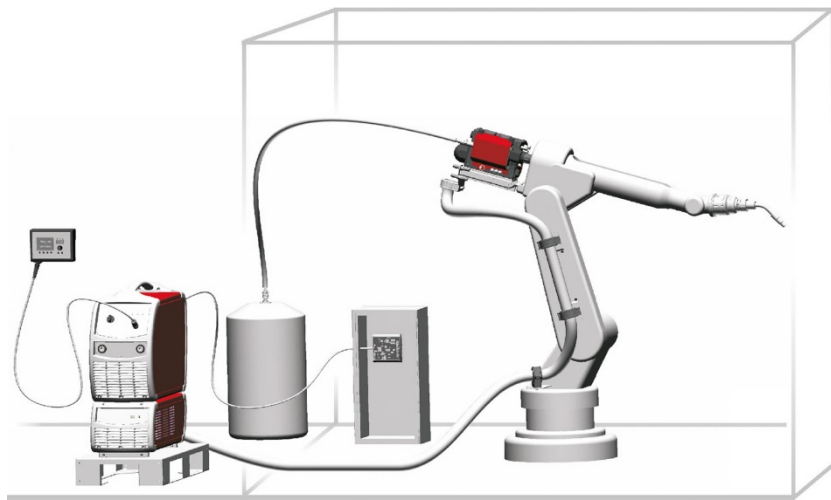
Equipos básicos de una estación robotizada de soldadura.
